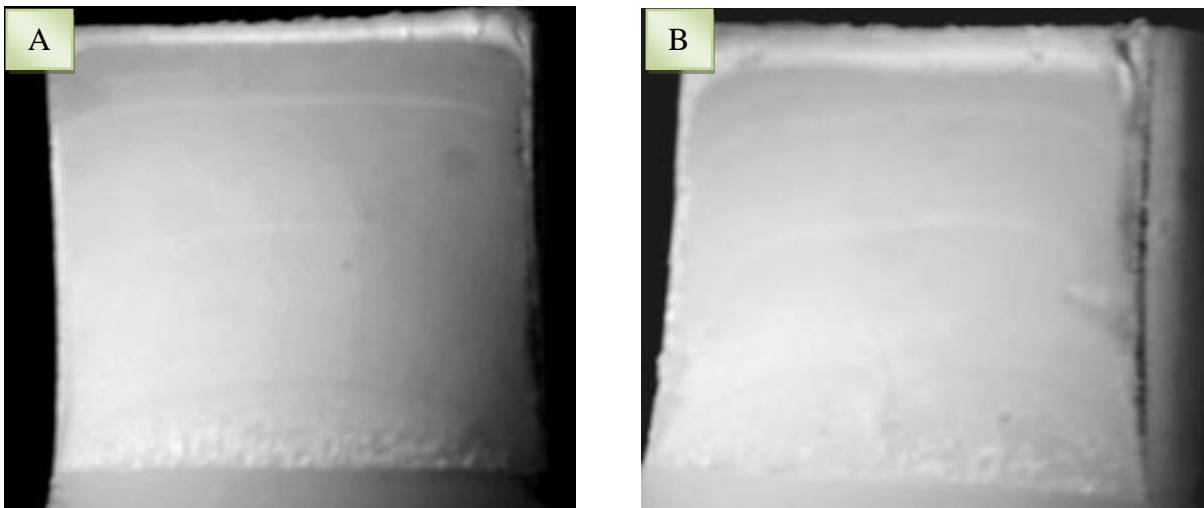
Superficie de fractura. A) MDPE; B) W-MDPE. Fractura ~ 0 °C.
